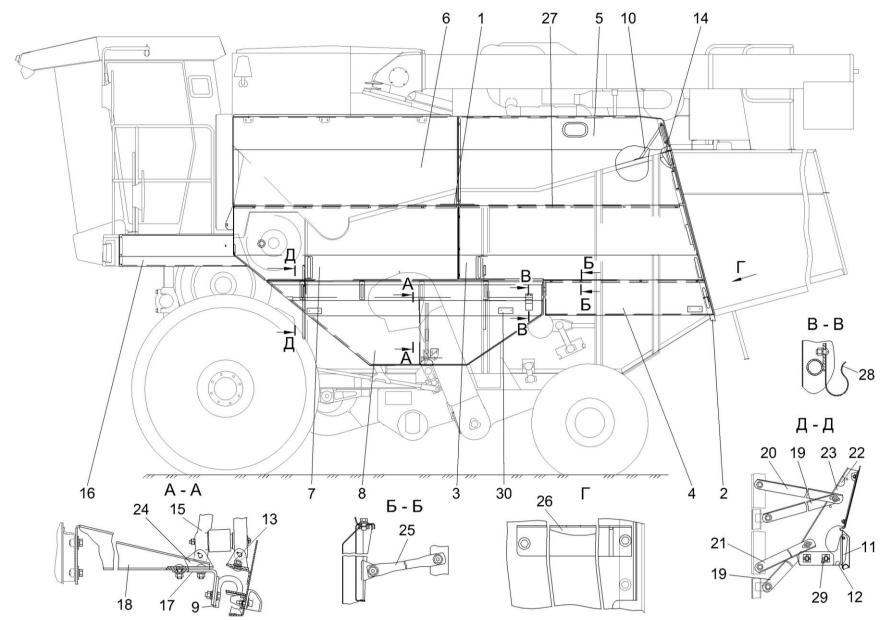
Установка капотов и ограждений КЗК-10-0128000Р2 (вид слева)
